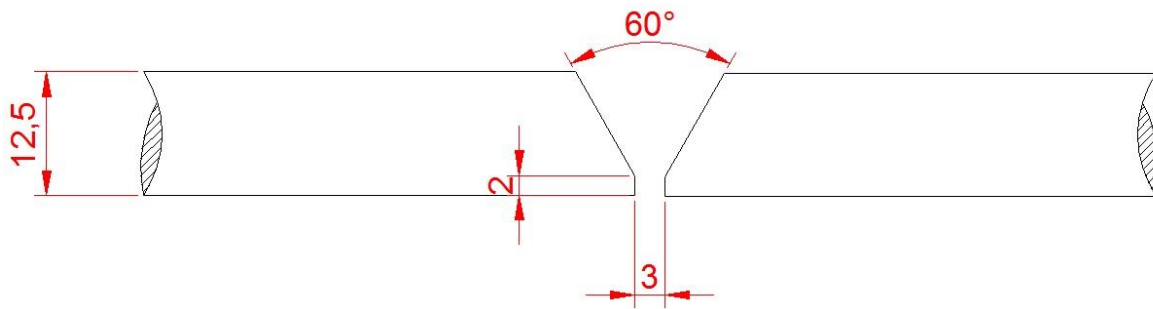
Junta de soldagem. Seção transversal. Escala em milímetros.
